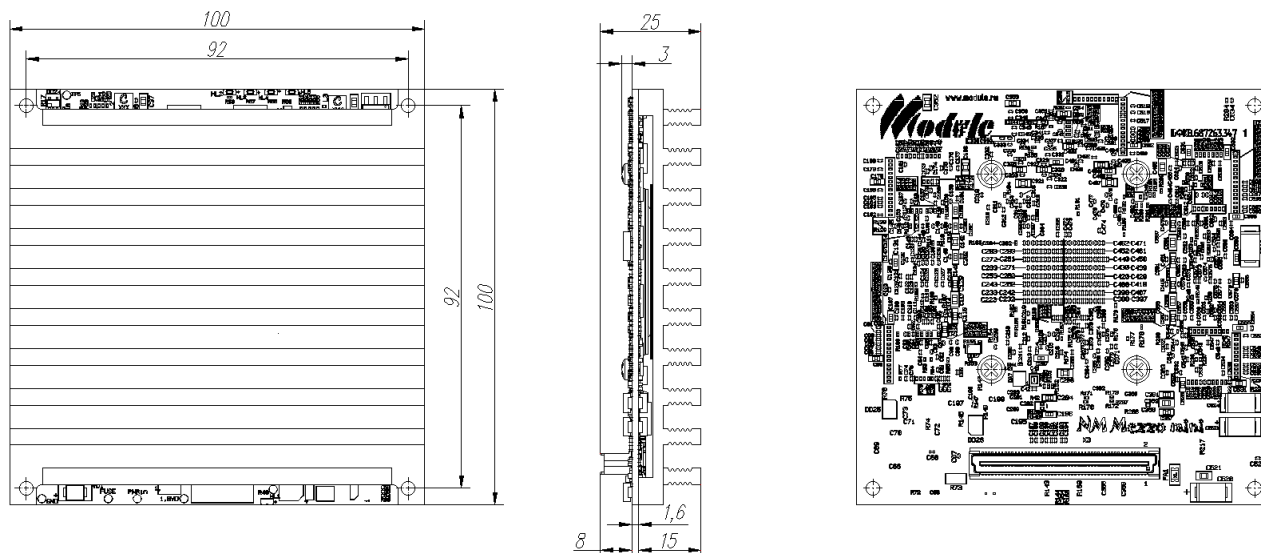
Габаритные и присоединительные размеры Модуля
